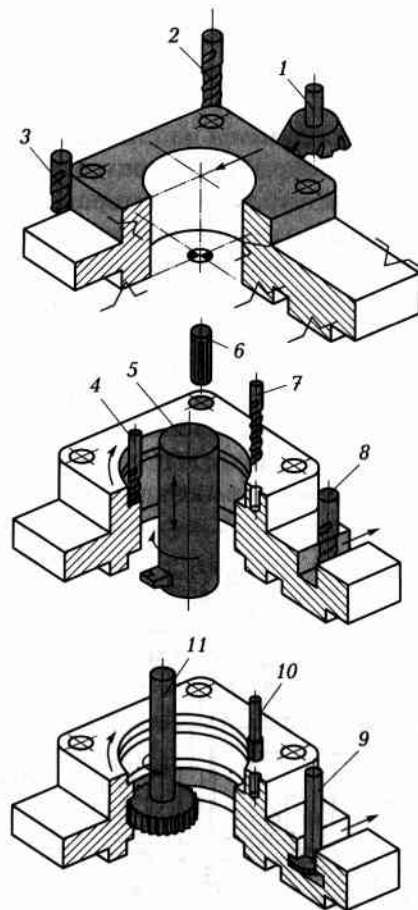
Схема технологических переходов, выполняемых при обработке заготовок корпусных деталей с одного установка на многоцелевом станке вертикальной компоновки:
